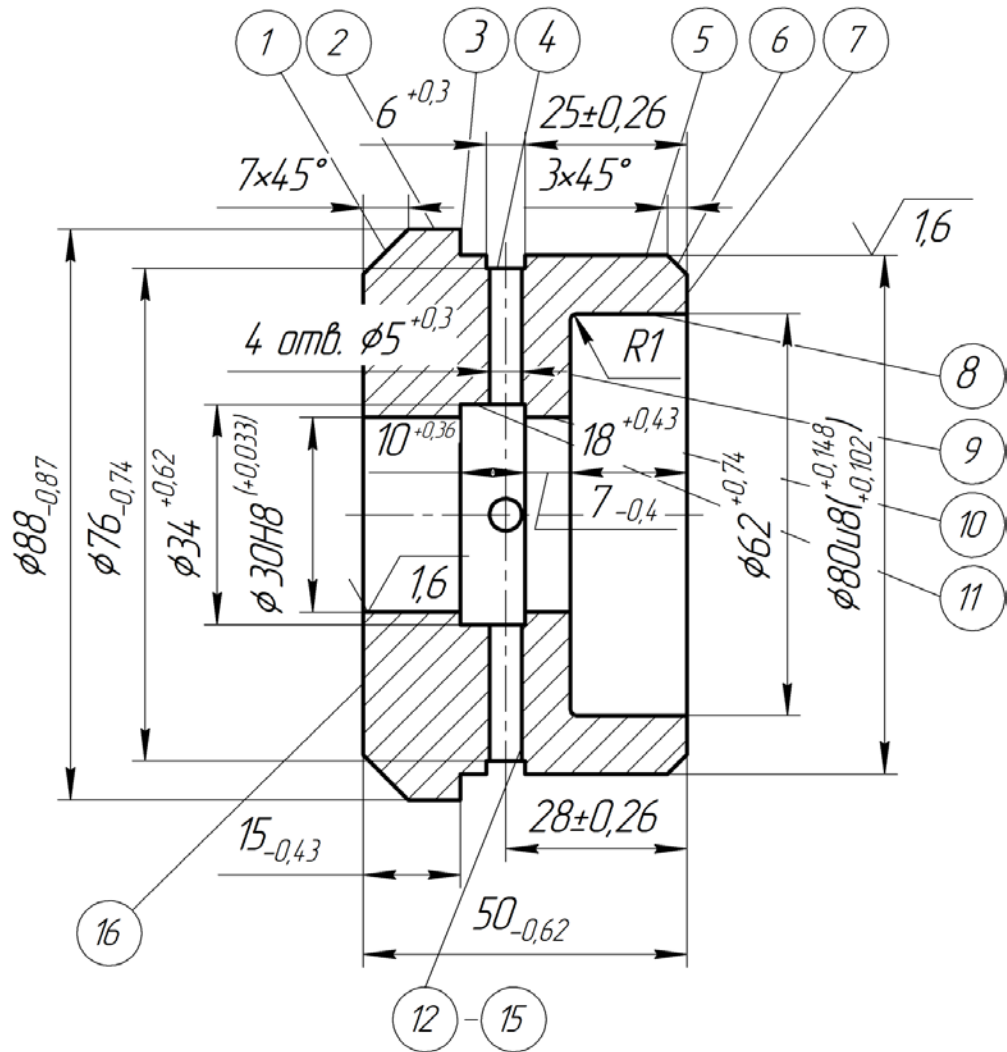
Ескіз деталі Втулка ПМ-298.22.003 з нумерацією поверхонь
